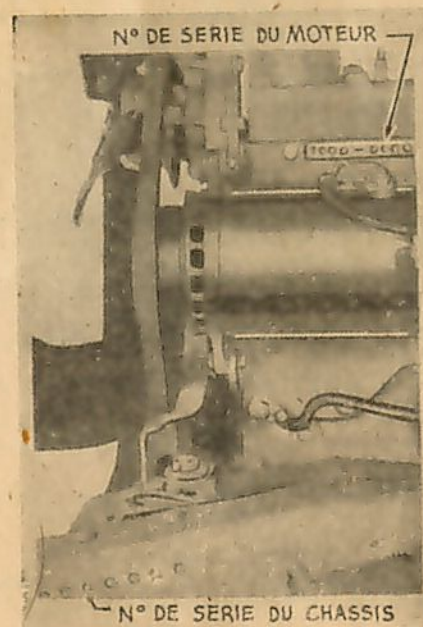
Emplacement des n° de série du châssis et du moteur.
